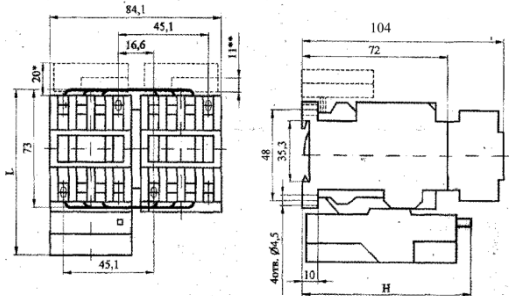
Пускатели реверсивные, степени защиты IP00, IP20
